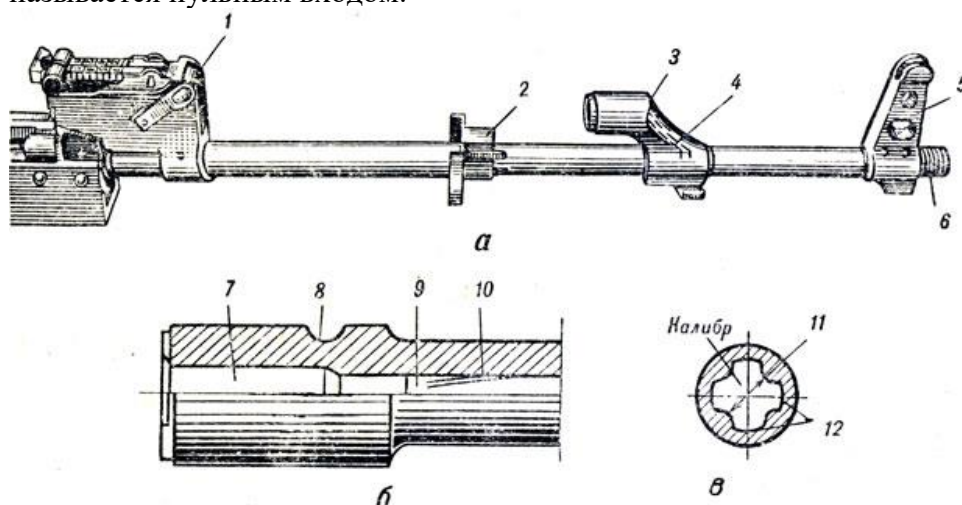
Ствол: а - общий вид; б - казенная часть в разрезе; в - сечение ствола; 1 - колодка прицела; 2 - соединительная муфта; 3 - газовая камера; 4 - газоотводное отверстие; 5 - основание мушки; 6 - резьба; 7 - патронник; 8 - выем для шпильки ствола; 9 - пульный вход; 10 - нарезная часть; 11 - поле; 12 - нарезы
